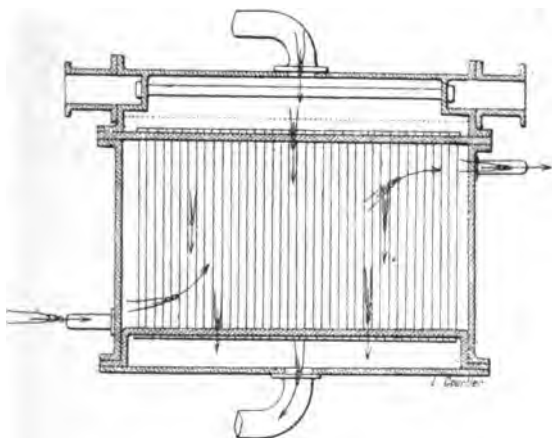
Condenseur à surface de Hall pour machine de terre.
